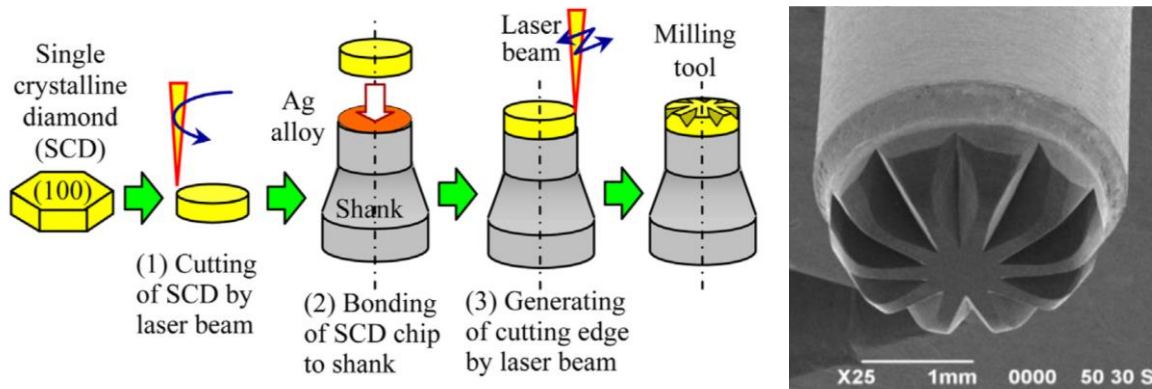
Mikroschleifwerkzeug aus Diamant [6]
